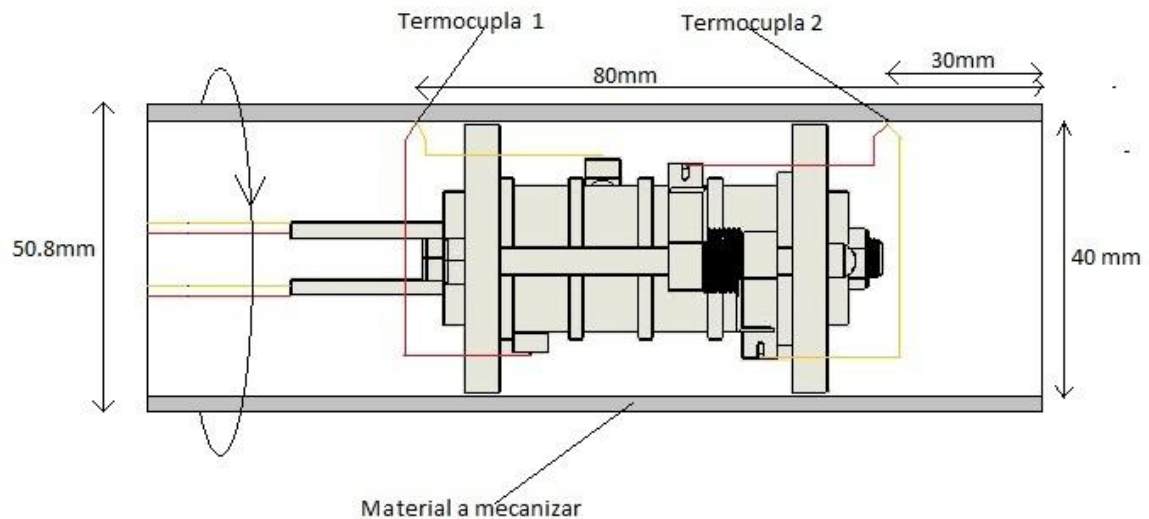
Esquema del montaje realizado en la pieza de trabajo.
